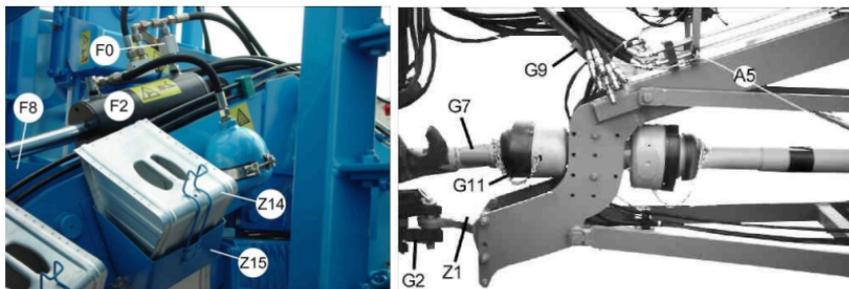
Установка фрезерного культиватора на хранение
